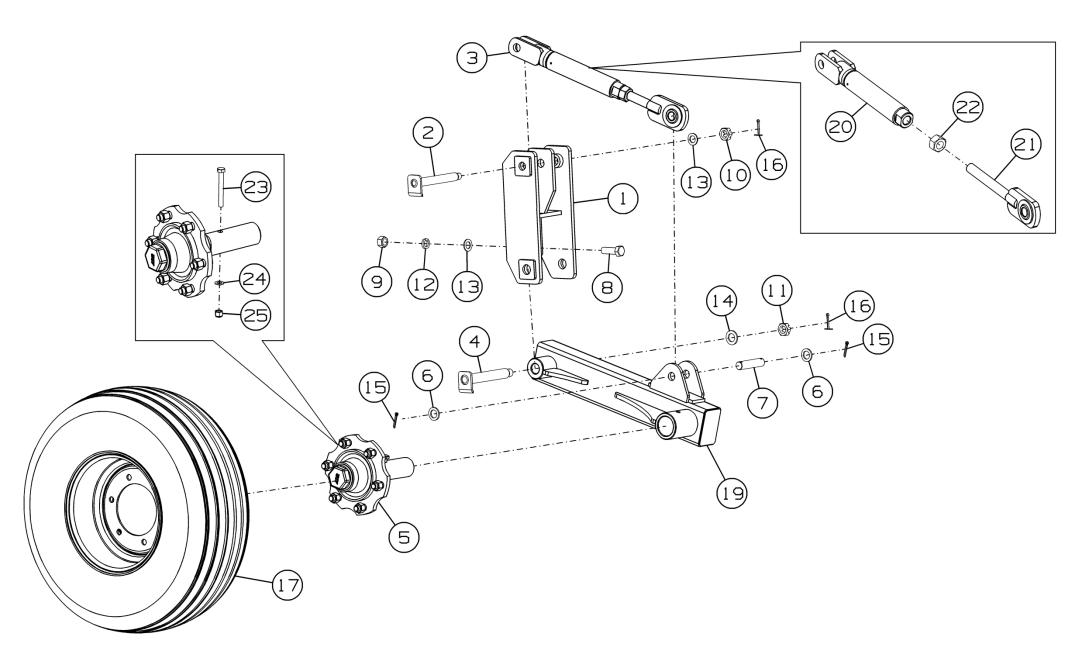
Колесо опорное СГ-122.06.000-01
